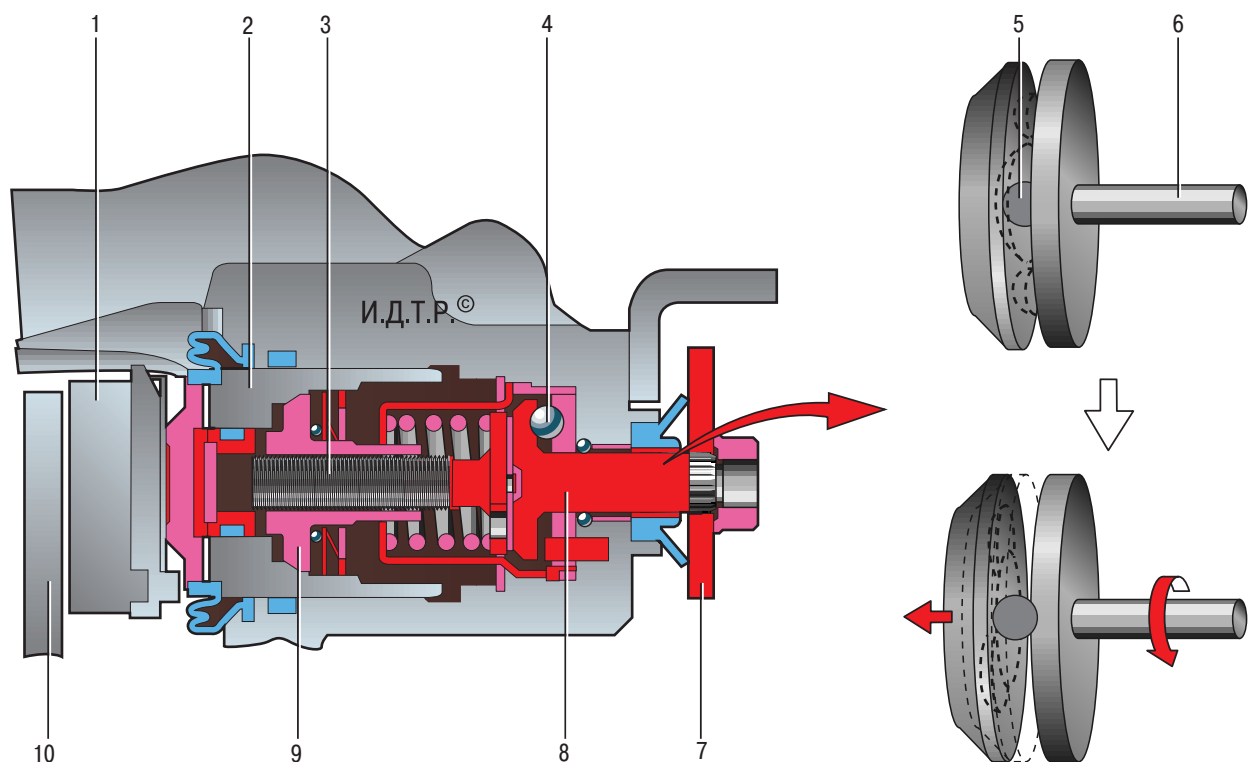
Схема работы стояночного тормозного механизма: 1 – колодка дискового тормоза; 2 – поршень; 3 – шток; 4, 5 – запорный шарик; 6, 8 – первичный вал; 7 – угловой рычаг; 9 – винтовая муфта; 10 – тормозной диск
